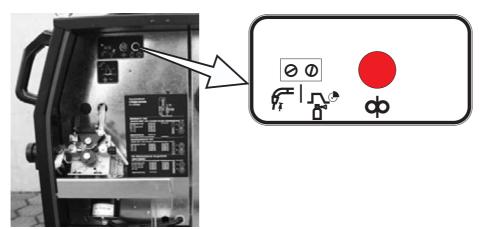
/2. Органы управления внутри сварочного аппарата или, соответственно, переносного устройства подачи сварочной проволоки.
